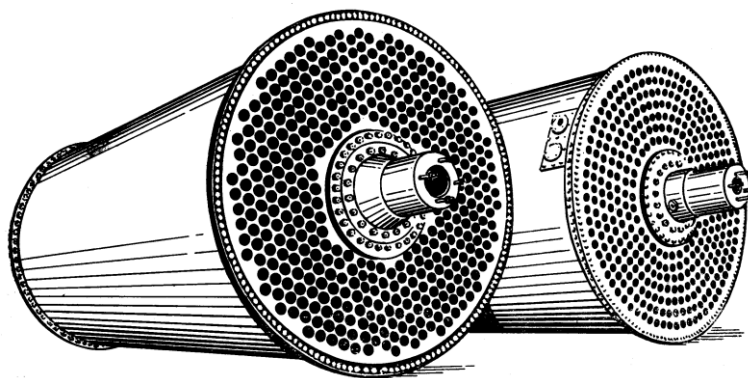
Загальний вид трубчатої барабанної сушарки
